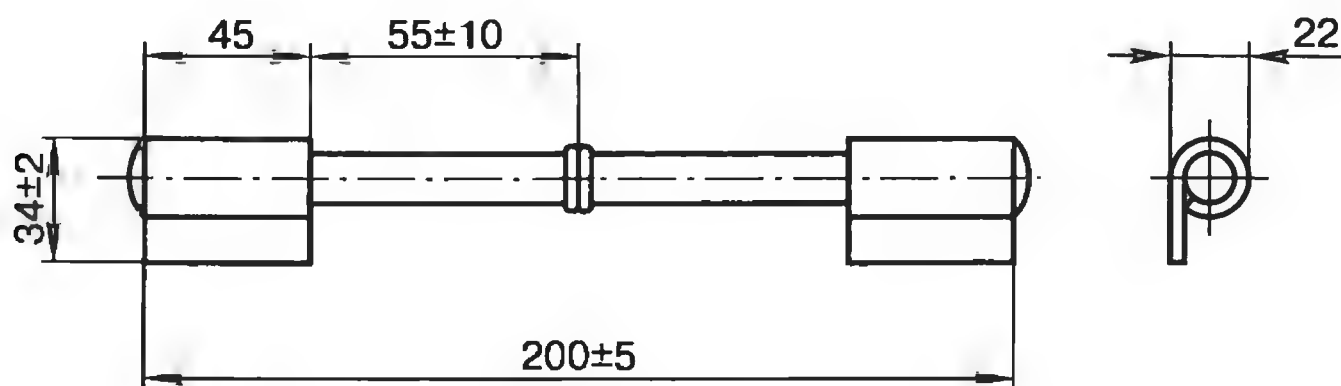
Соединитель рельсовый стыковой медный приварной фартучного типа РЭСФ
